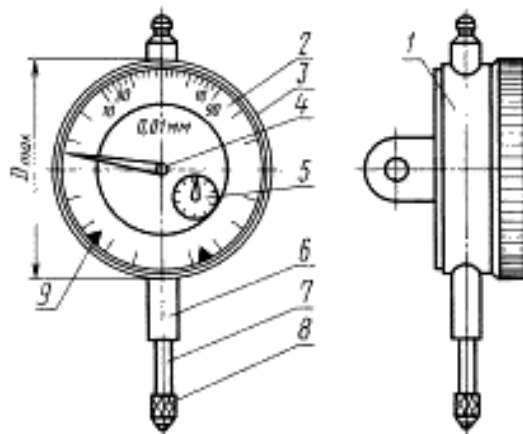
Индикатор часового типа марки ИЧ-10 с перемещением измерительного стержня параллельно шкале:
